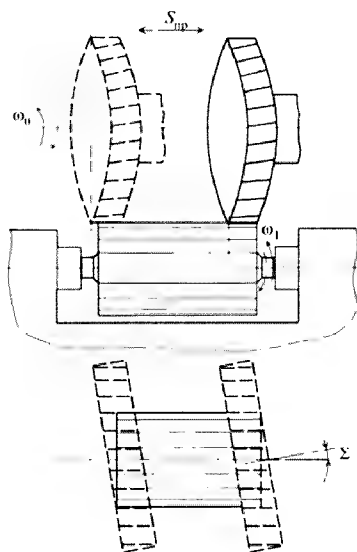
Схема операции обработки зубчатого колеса шлифовальным шевером
